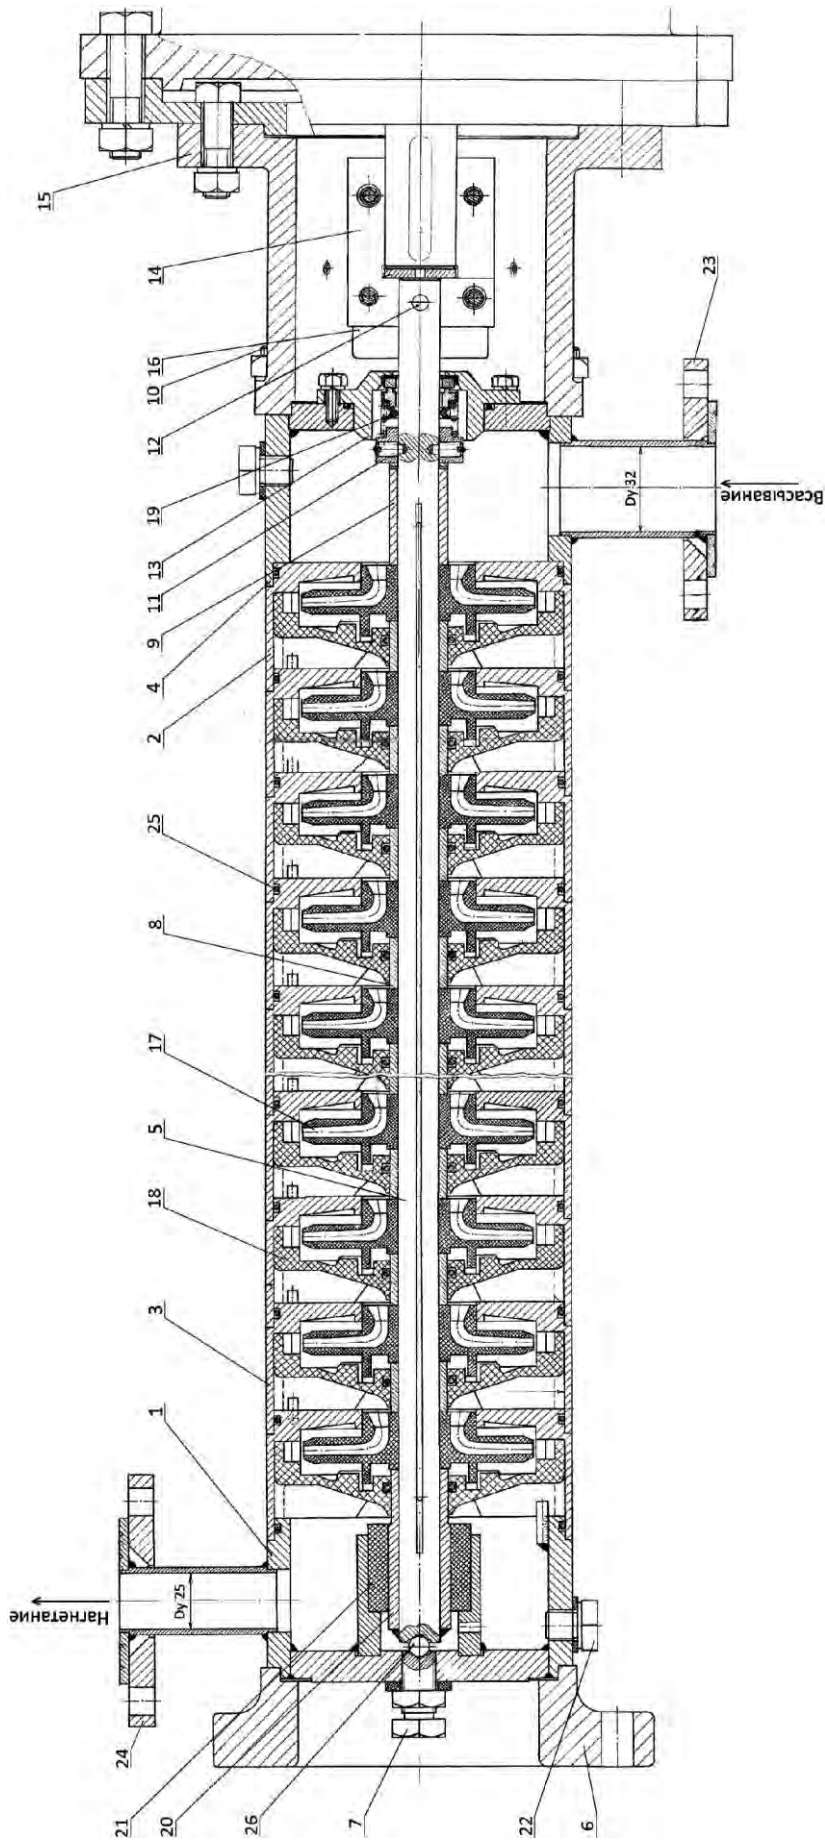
Общий вид электронасосного агрегата ЦНС(ПА)
